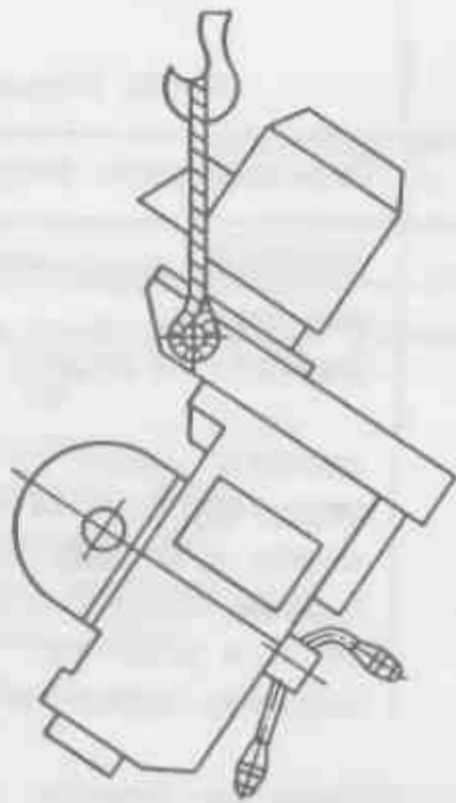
Схема транспортировки шпиндельной головки станка 6Т80Ш
